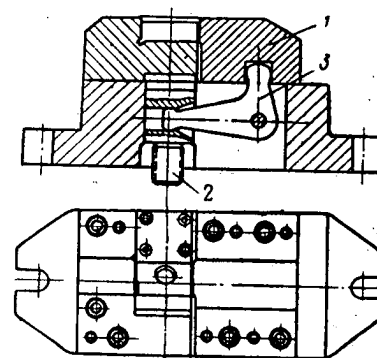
Групповое приспособление для фрезерования гребня и полок кронштейна.
